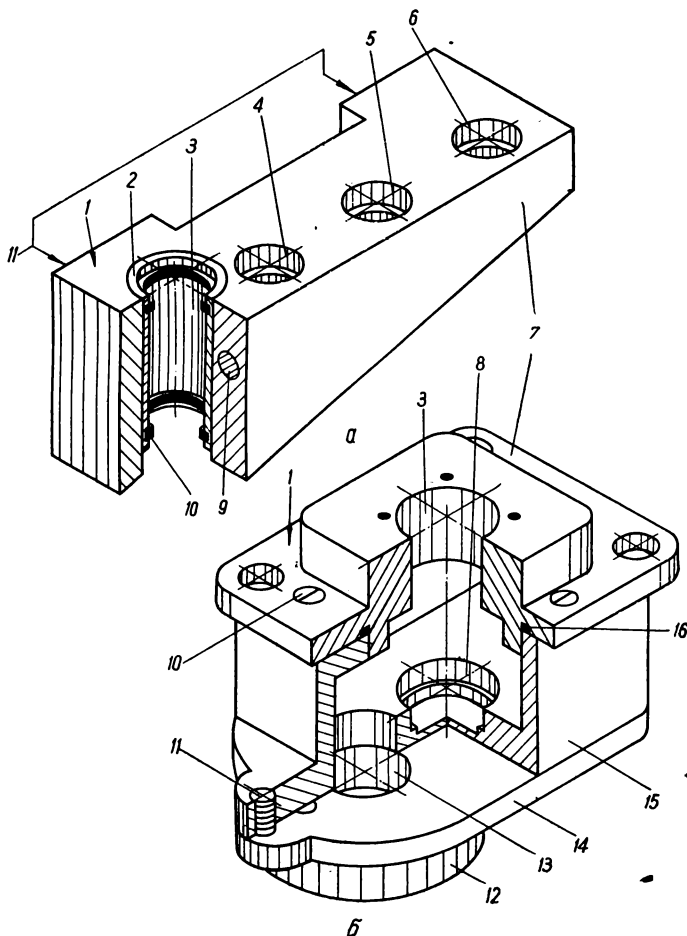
Конструкции несущих корпусов объемной формы блоков рабочих зон неразъемного (а) и разъемного (б) исполнений.
